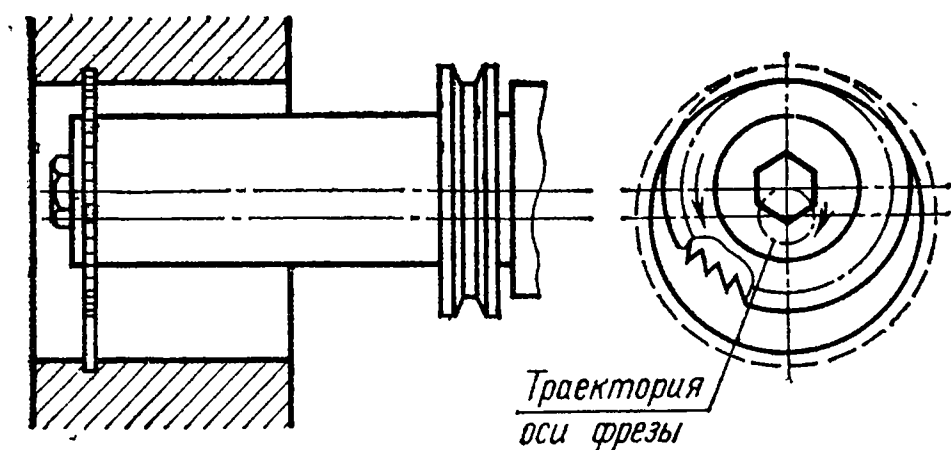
Фрезерование кольцевой канавки в режиме круговой интерполяции
